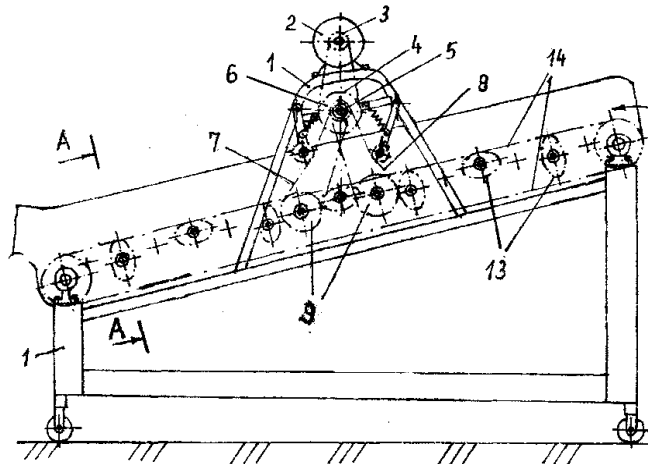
Общий вид машины для сухой очистки картофеля и клубнеплодов:
